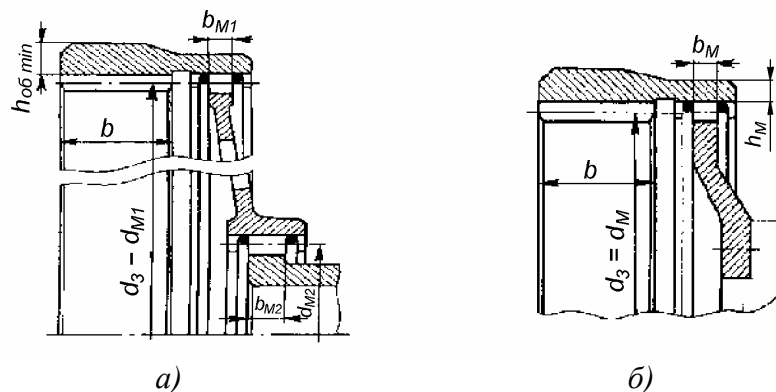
Плавающие вращающиеся центральные колеса с внутренними зубьями
